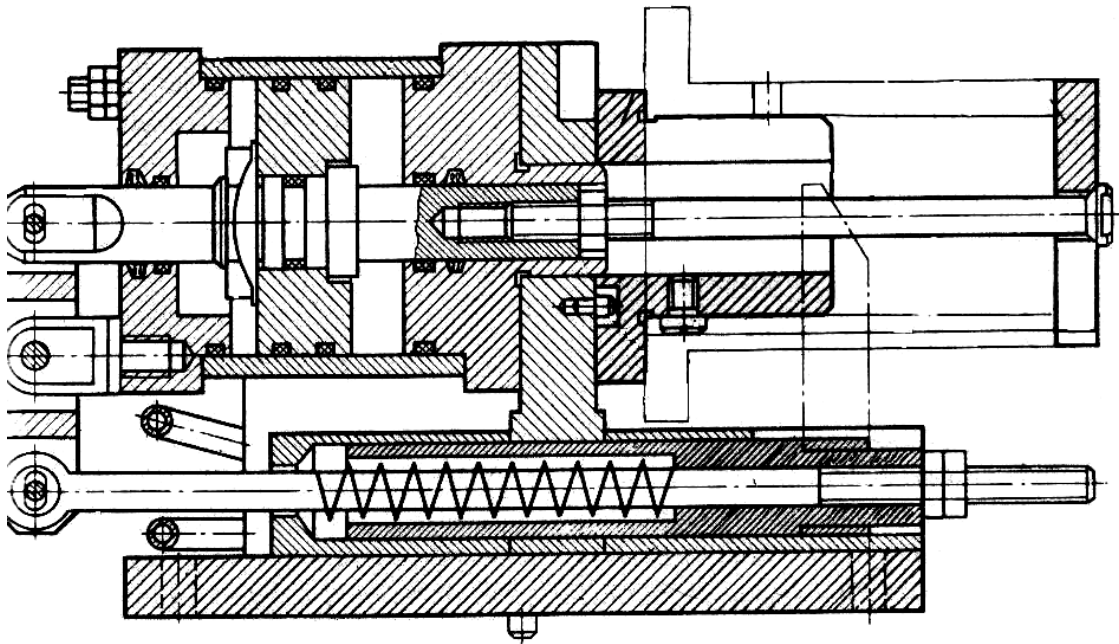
Приспособление СМП для обработки деталей типа втулок
